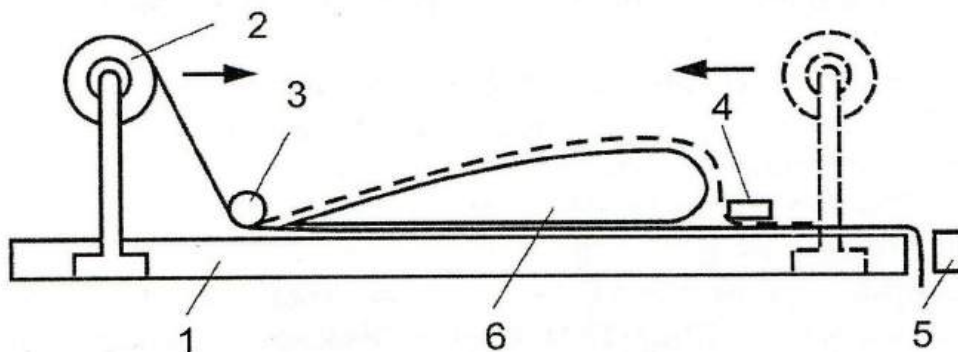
Схема упаковки вузлів клеєної конструкції:
